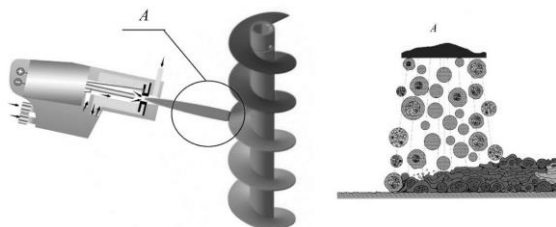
Обобщенная схема плазменного напыления винтовой и цилиндрической поверхностей шнека
